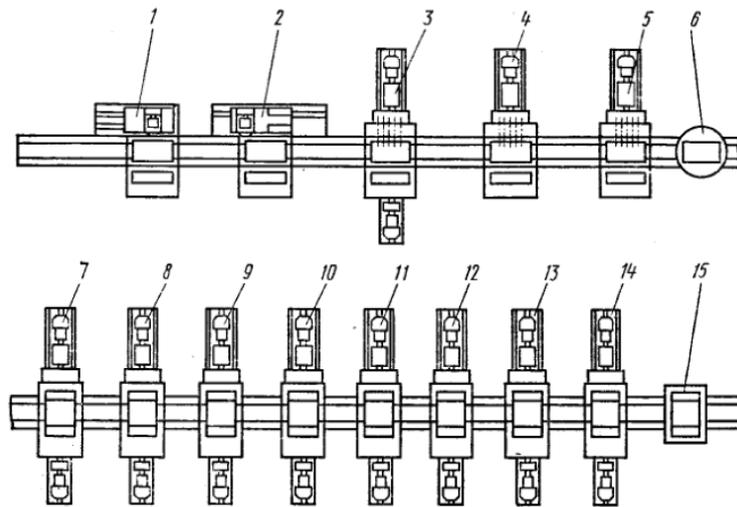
Планировка автоматической линии для обработки корпусных деталей:
